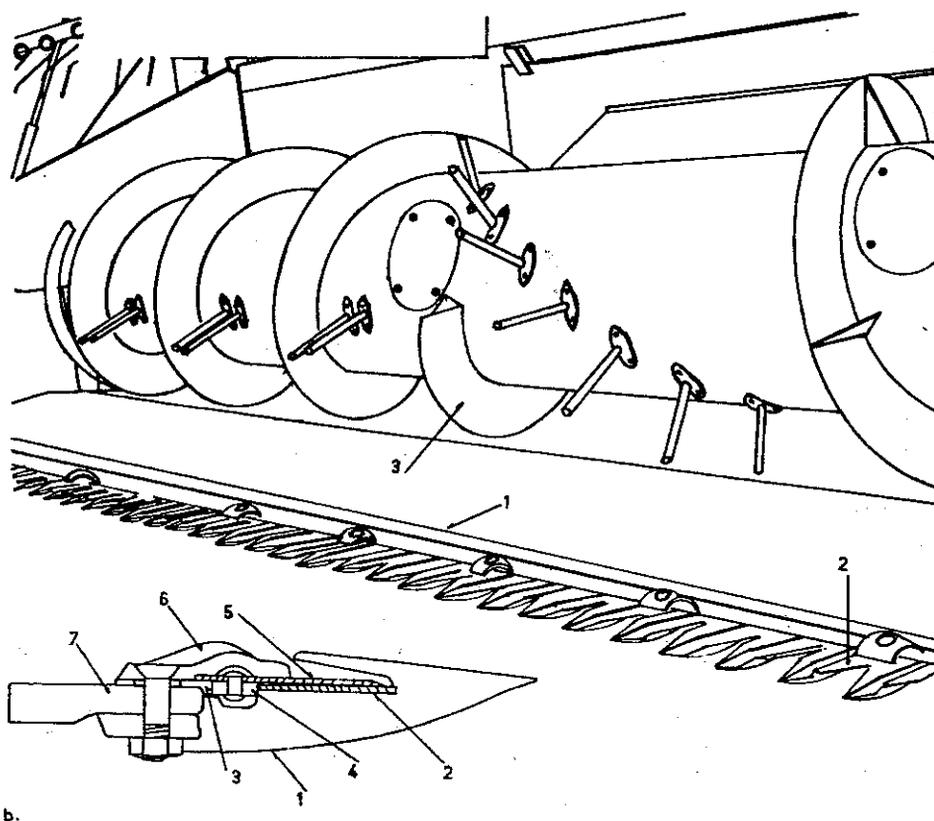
Barra de corte de uma colhedora: a) vista geral de uma barra de corte; 1) barra, 2) faca, 3) condutor helicoidal. b) detalhe de construção da barra; 1) guarda, 2) placa de apoio, 3) placa de desgaste, 4) barra da faca, 5) seção da faca, 6) grampo, 7) barra de suporte
